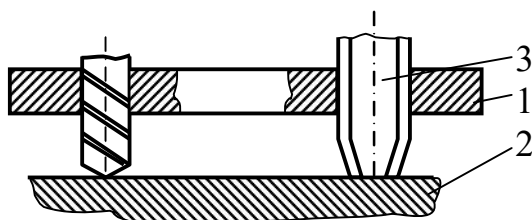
Використання кондукторної плити (1) при обробці заготовки (2) осьовим інструментом (3)
